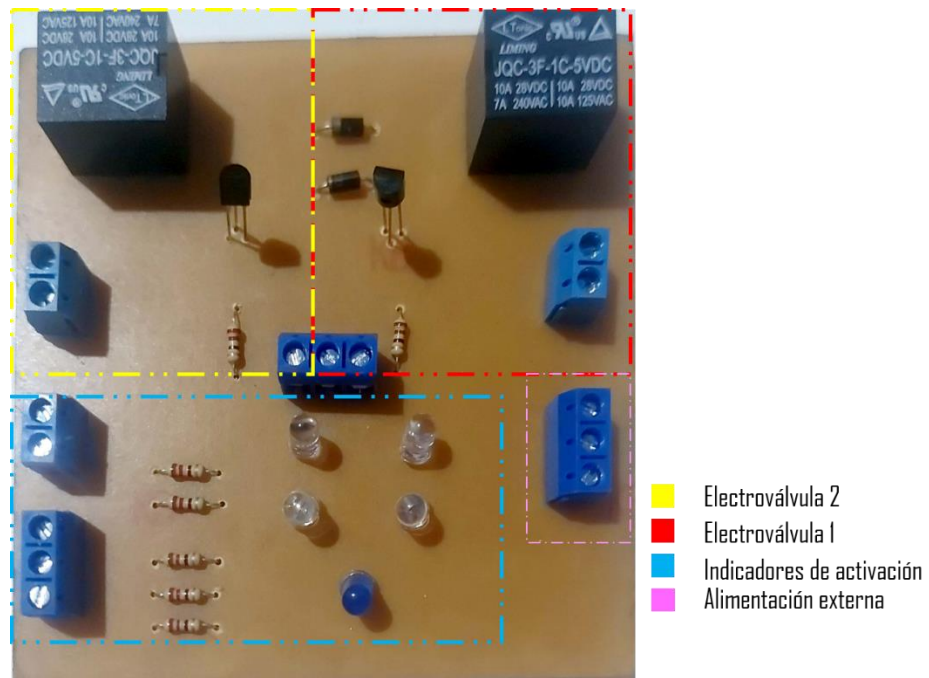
Circuito del sistema de control de riego en pcb. [Autor]
